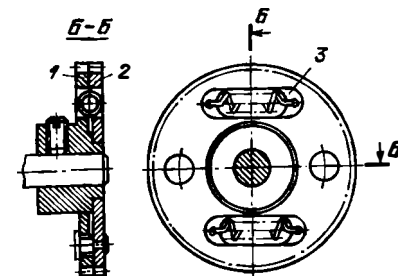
Разводное зубчатое колесо: 1 и 2 — зубчатые колеса; 3 — разводящая пружина
